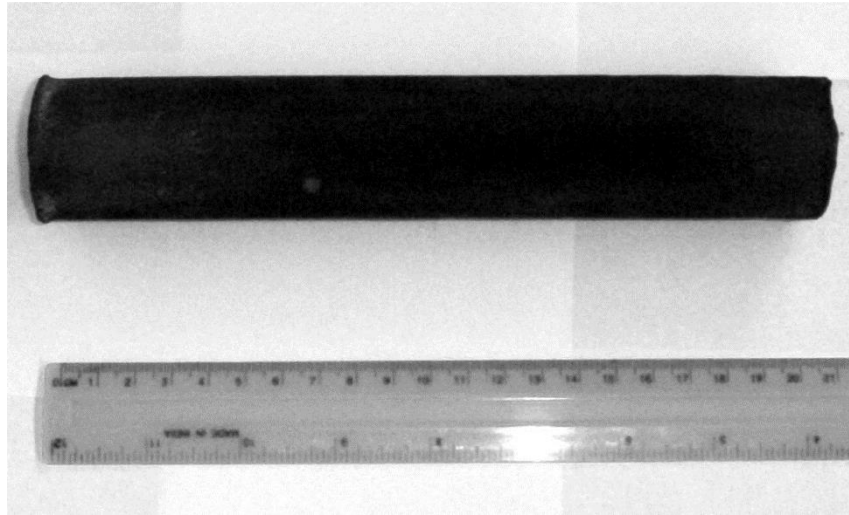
Загальний вигляд ППМ виготовленого з порошку ШХ15
